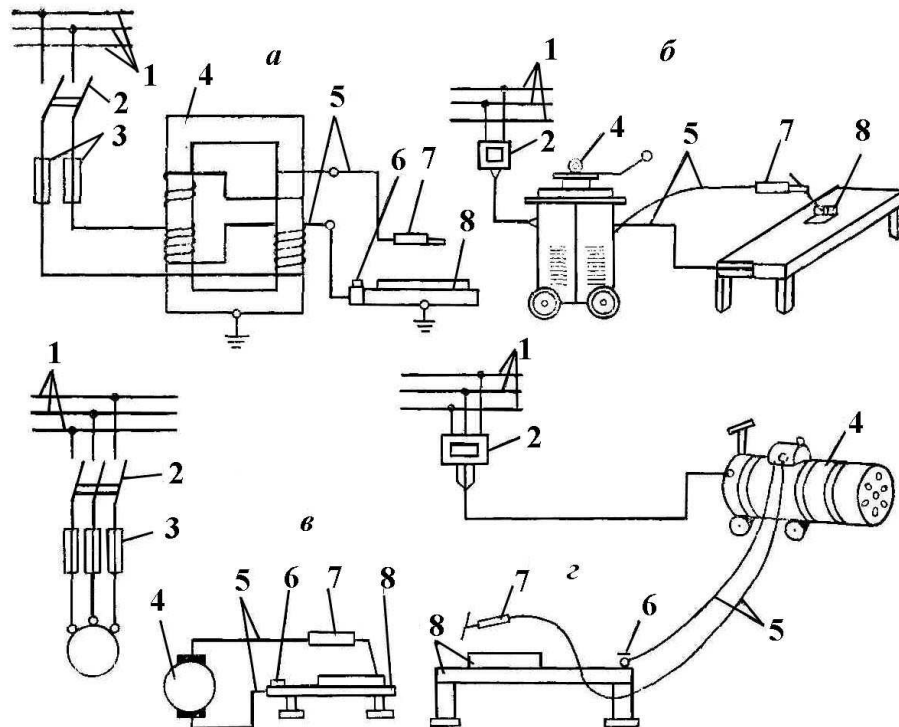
Пристрій для ручного електродугового зварювання:
